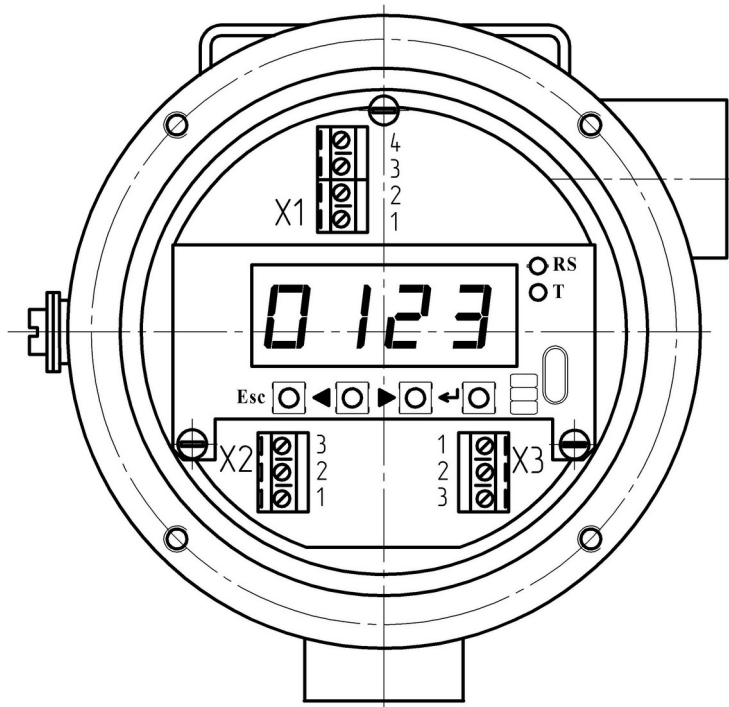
Внешний вид электронного блока ПП в корпусе «Н»
